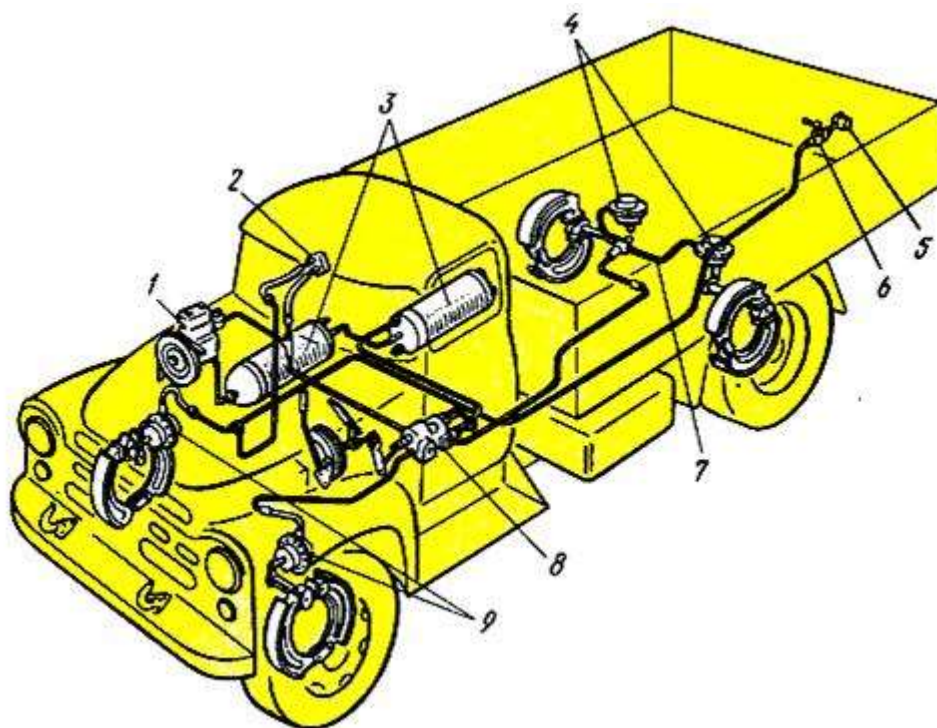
Схема пневмопривода тормозов автомобиля ЗИЛ-130 выпуска до 1984 г.
